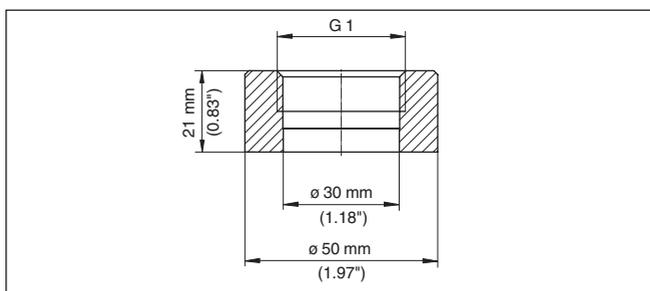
Dimensiones racor para soldar G1 (ISO 228-1) - VEGABAR 82, 83
